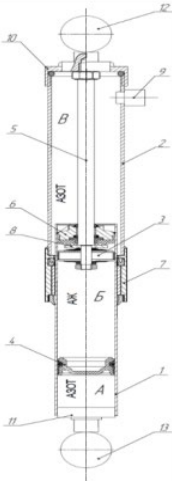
Экспериментальный амортизатор: 1 – цилиндр, 2 – резервуар, 3 – гидравлический поршень, 4 – разделительный поршень, 5 – шток, 6 – направляющая втулка, 7 – уплотнительно-направляющая втулка, 8 – стопорное кольцо, 9 – ниппель, 10 – верхняя крышка, 11 – нижняя крышка, 12, 13 – проушина
